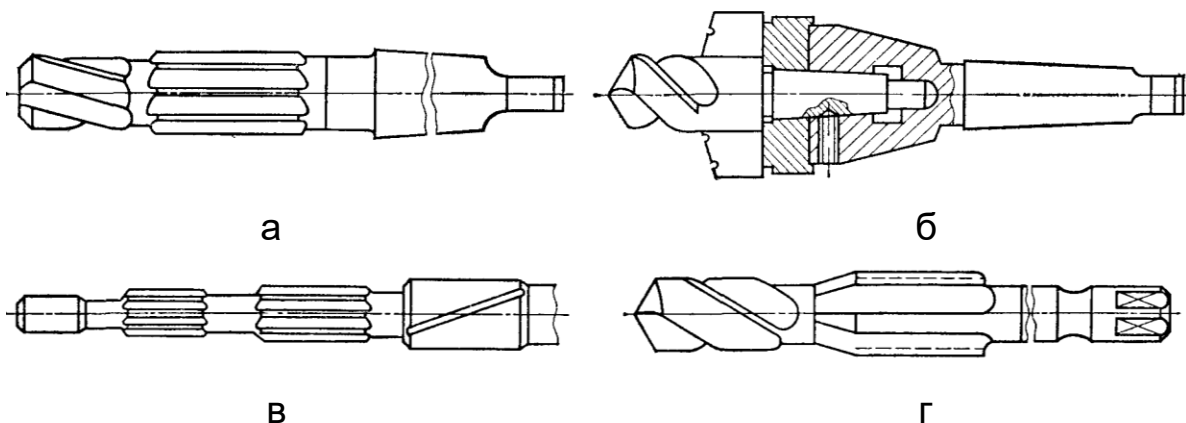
Комбинированные инструменты: а – зенкер-развертка; б – сверло-сверло; в – развертка-развертка; г – сверло-метчик
